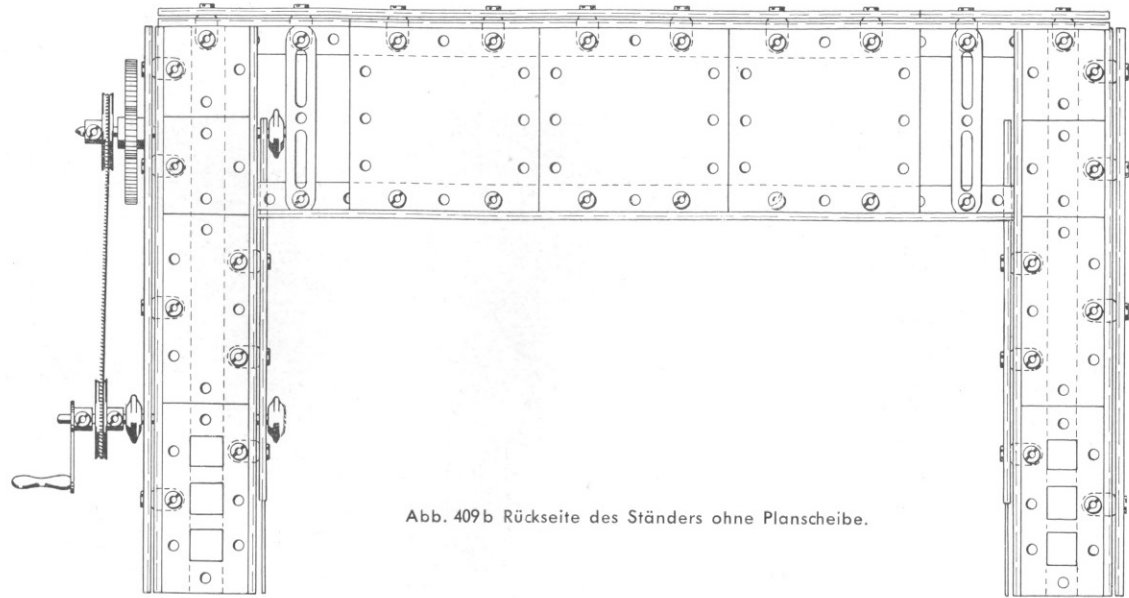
b Rückseite des Ständers ohne Planscheibe.
